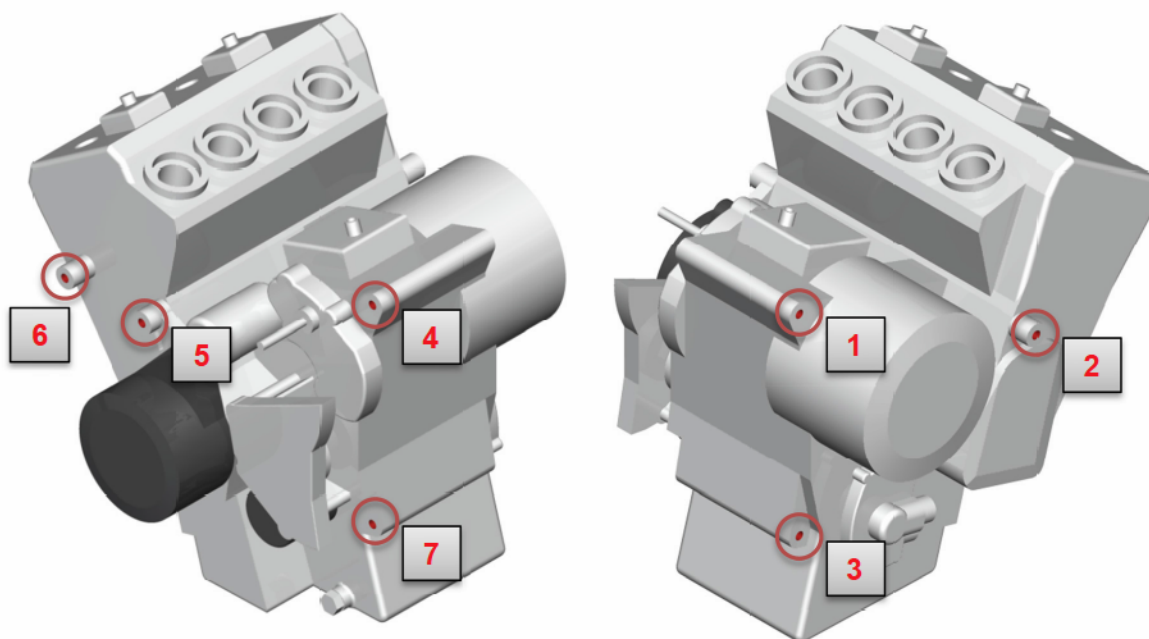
Motor Yamaha FZ6 Fazer - typ J507E
